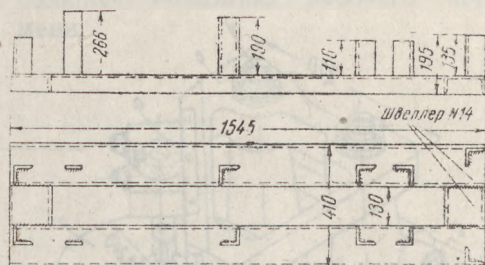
Сборочно-сварочный кондуктор рам рыбонасосной установки РБ-100.
